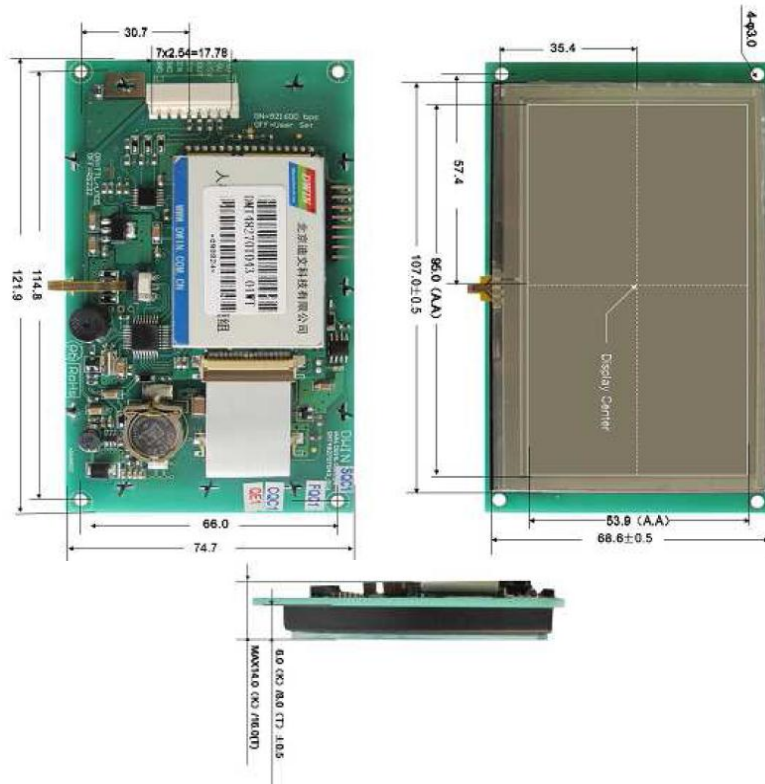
Dimensiones físicas de la pantalla táctil
